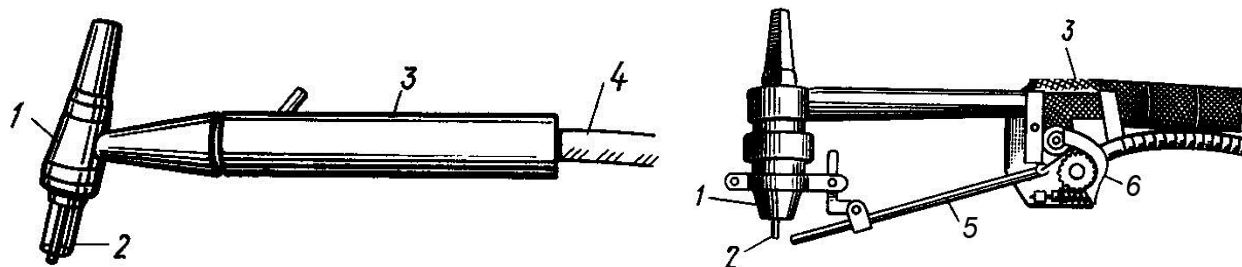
Схеми установок для аргоно-дугового зварювання
